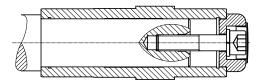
riduttore fissato ad un albero con spallamento mediante elemento di fissaggio
